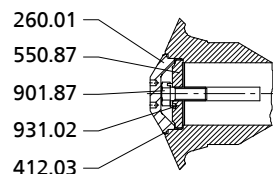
Крепление рабочего колеса для подшипниковых кронштейнов S06, S07 и S08, кроме типоразмера Sewatec 500-632
